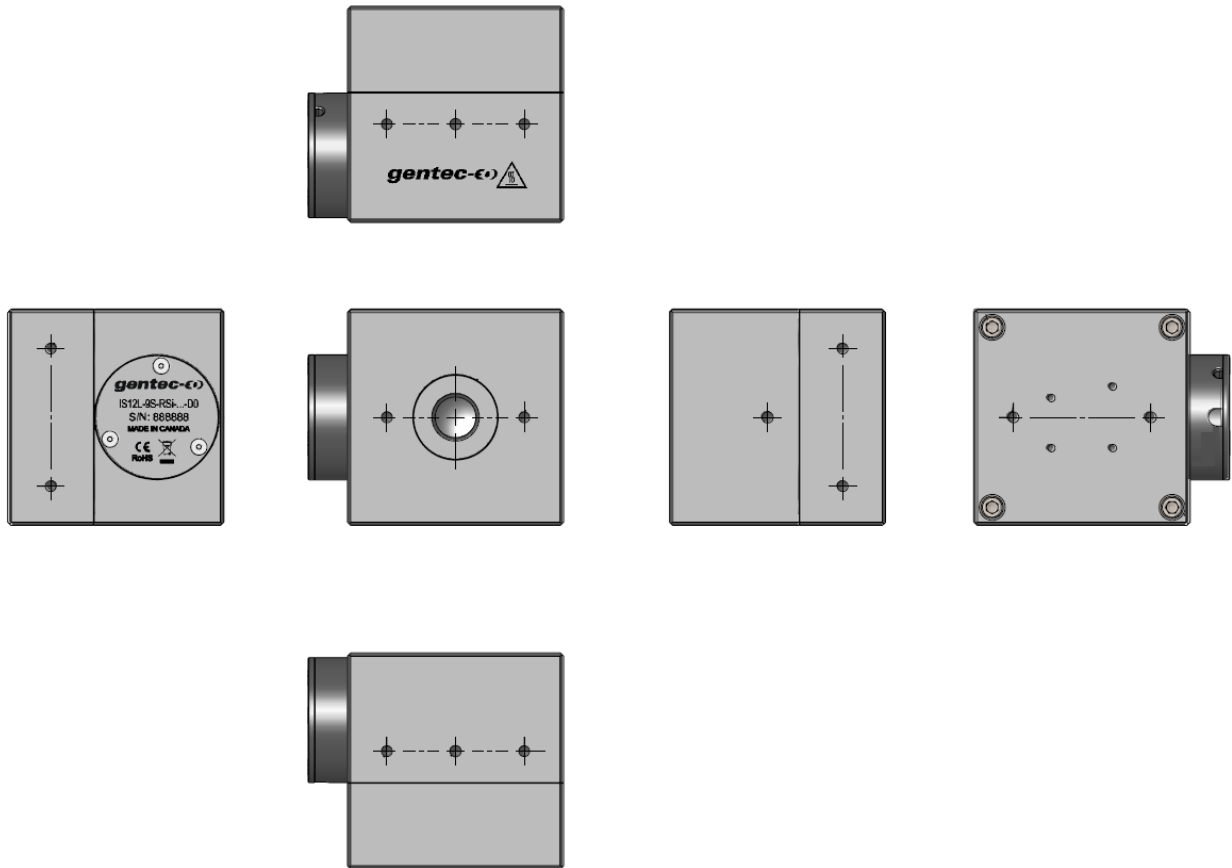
Dessin d'encombrement, IS12L-9S-RSi-INT/IDR-D0.
